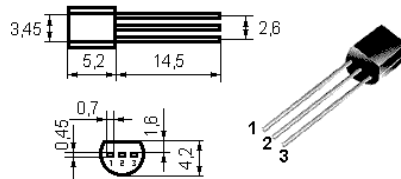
Габаритні розміри транзистора 2N3905
